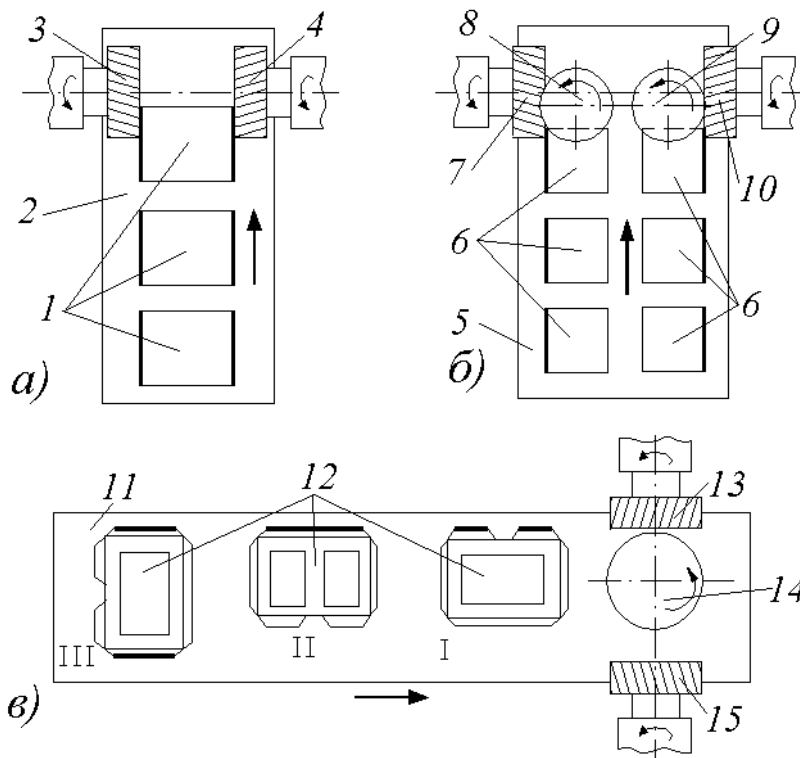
Схемы фрезерования на продольно-фрезерных станках
